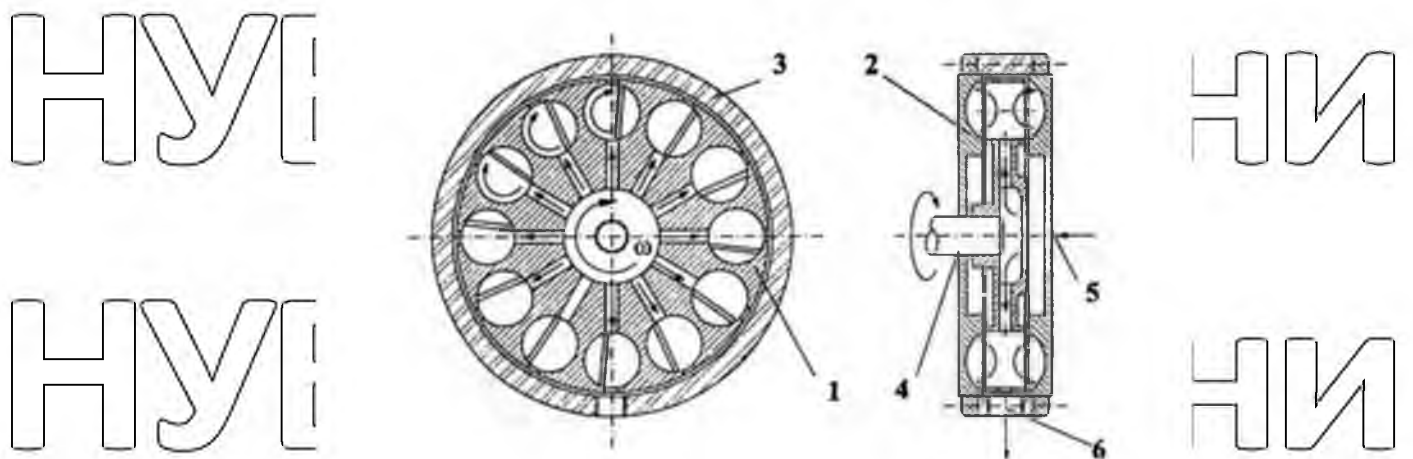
Схема гідродинамічного нагрівача ДДТУ: 1 – ротор; 2 – корпус; 3 – обід; 4 – вал приводу; 5 і 6 – вхід і вихід для молока
